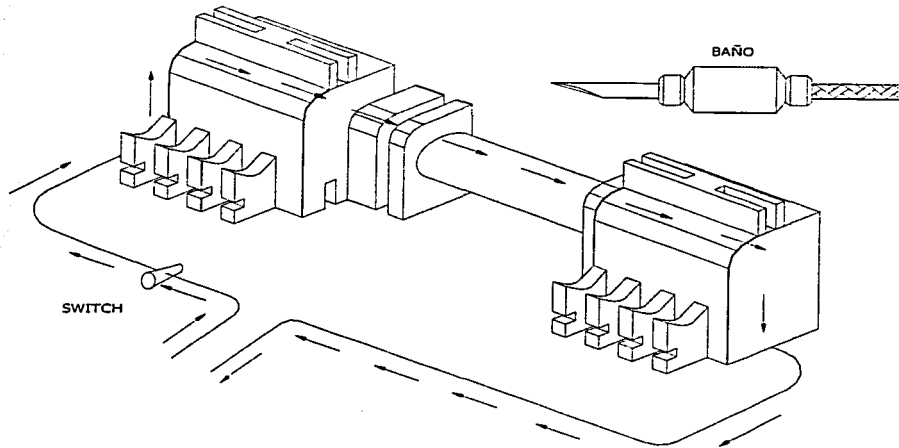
Magnetización por contacto directo. En la magnetización por contacto directo se hace pasar la corriente de "lado a lado" a través de la parte a ser examinada, lo que produce un campo magnético circular al flujo de la corriente. Las flechas indican el sentido del flujo de corriente.
